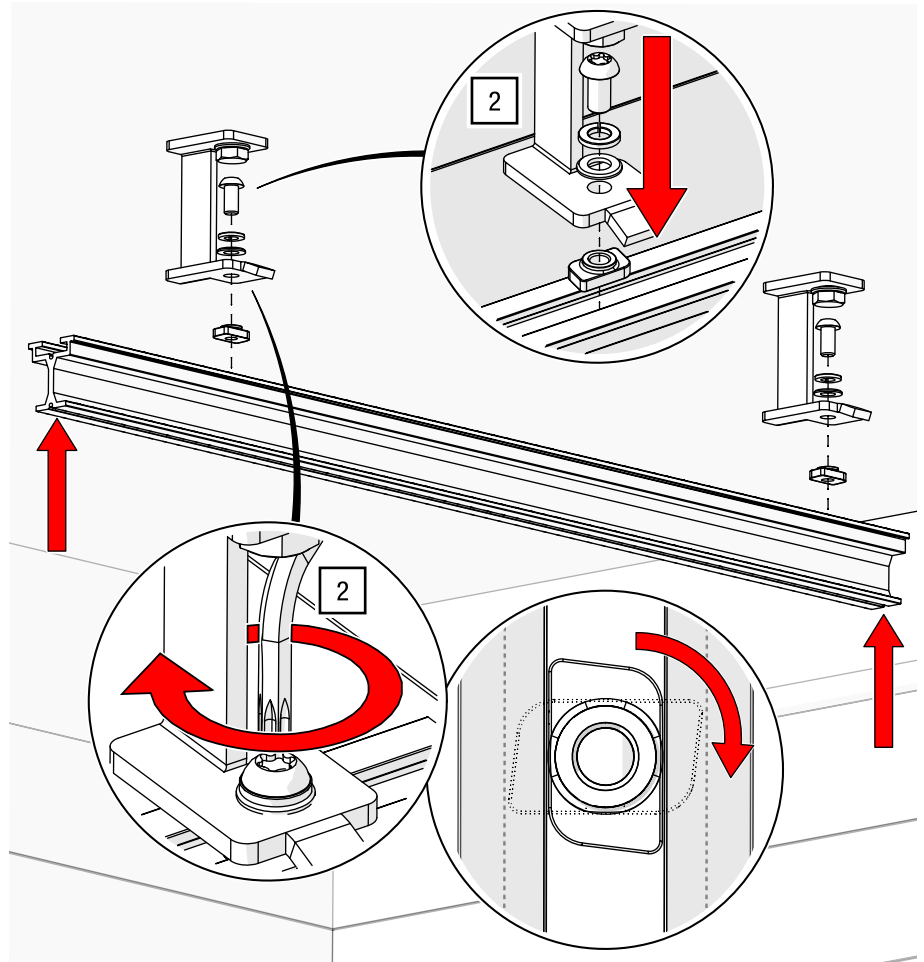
Abhängung für Seilführung – Schiene verschrauben
